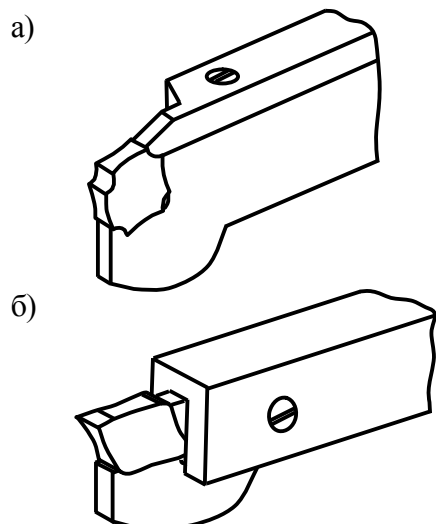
Новые конструкции отрезных резцов с механическим креплением предлагаемых многогранных неперетачиваемых пластин
